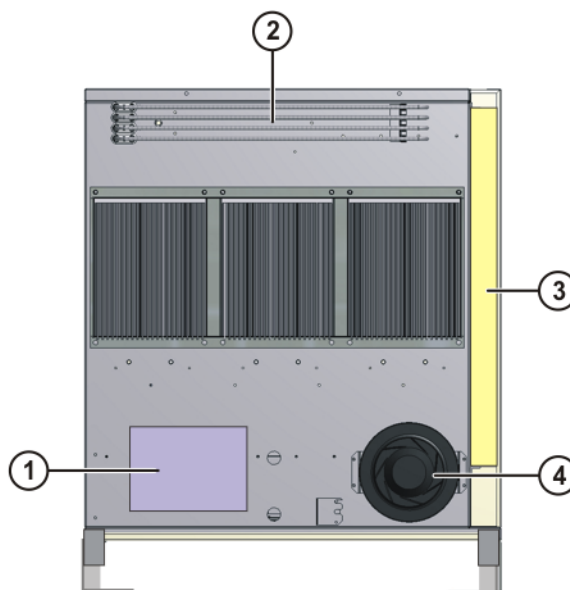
Aperçu de la commande de robot, vue arrière
